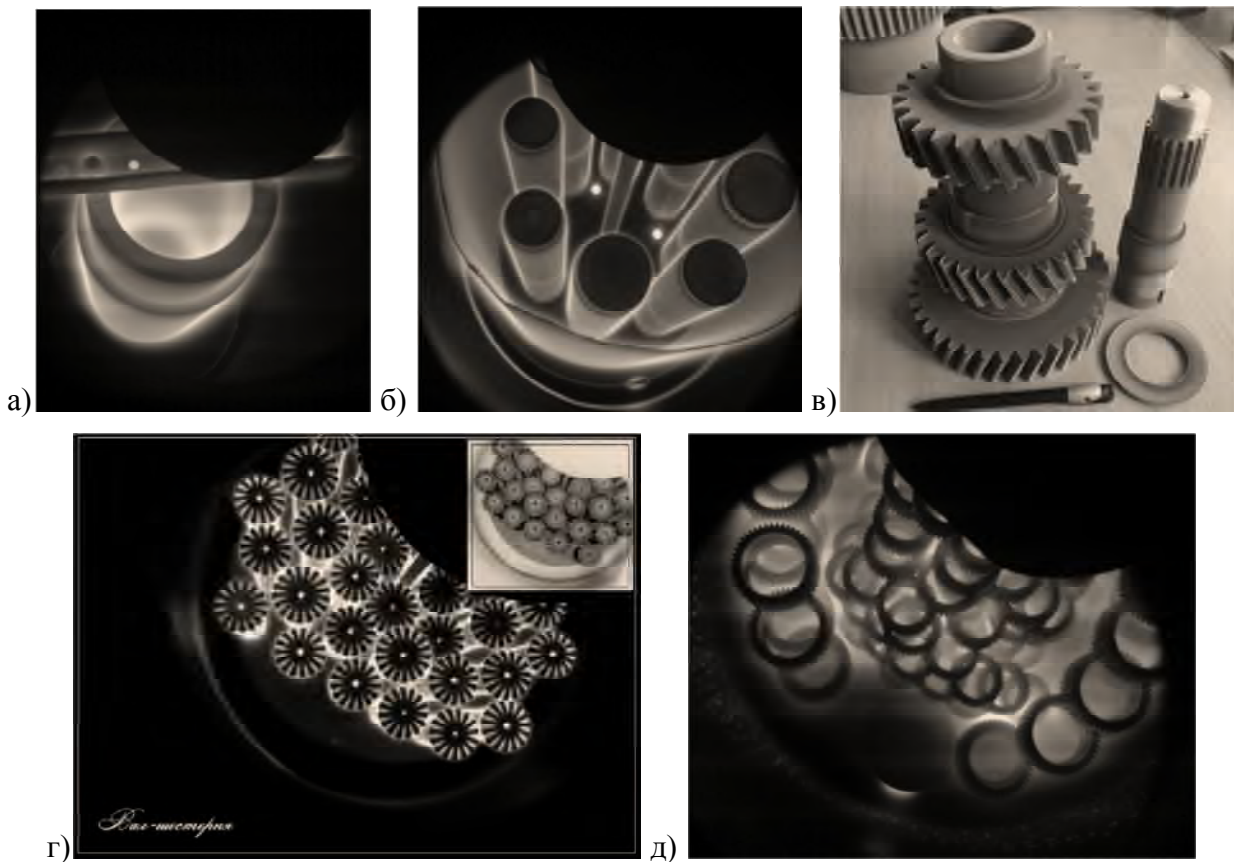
Применение ИПТА для некоторых деталей: а) гильза; б) шпиндель; в) шестерня и вал-шестерня; г) вал-шестерня; д) зубчатые колеса
